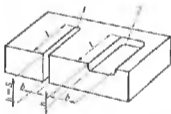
Разделительный (1) и поверхностный (2) резы:
